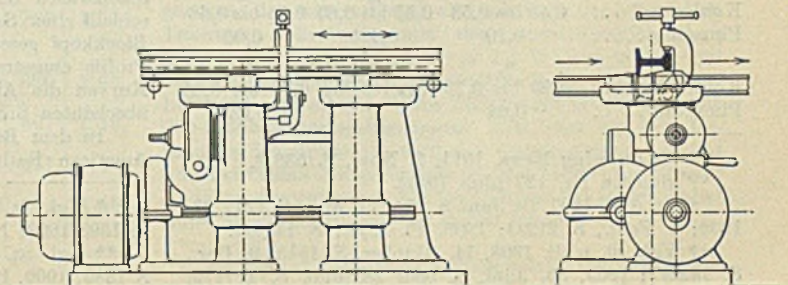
Bohrmaschinen für die Stemmlaschenlöcher.
